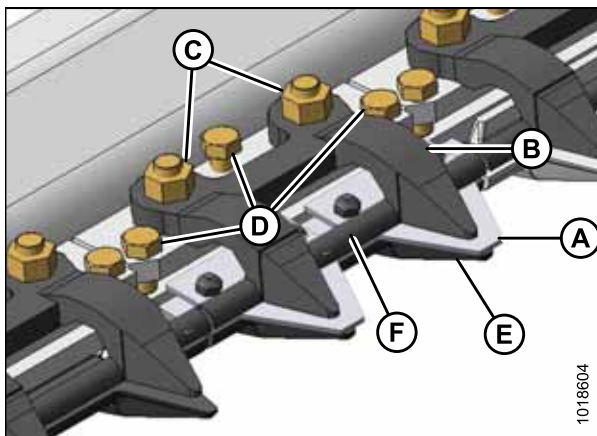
Стандартный кованый прижим укороченного противорежущего пальца
